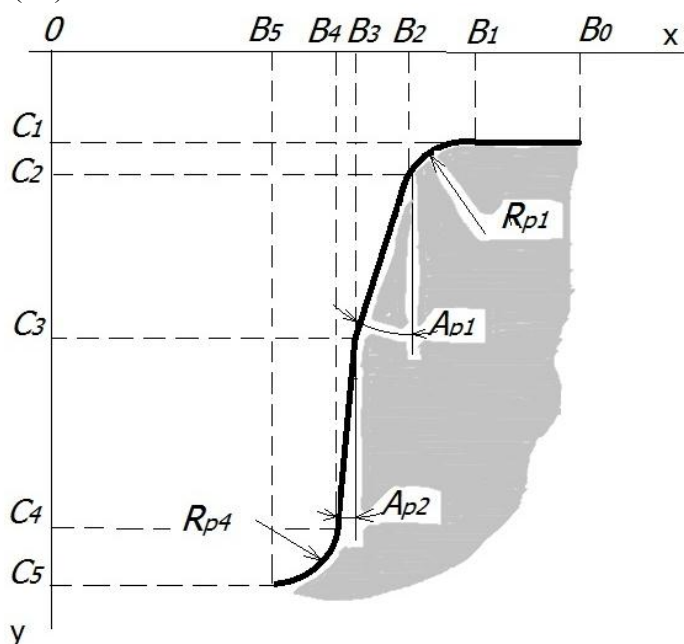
Схема параметров профиля зуба рейки колесно-реечного движителя
